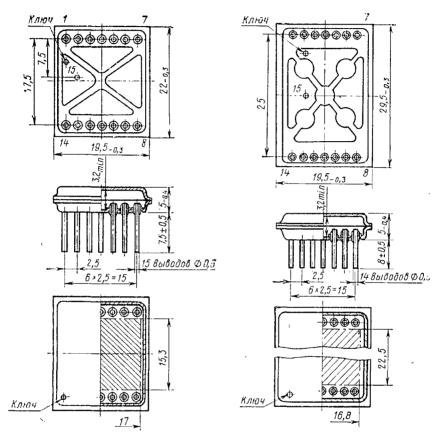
Конструкция металлостеклянного корпуса 1206 (153.15-1)
